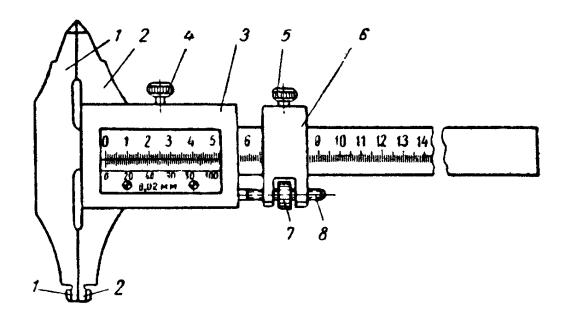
Внешний вид штангенциркуля ШЦ-II: 1 и 2 – губки с кромочными (сверху), плоскими и круглыми (внизу) измерительными поверхностями; 3 – рамка со шкалой нониуса; 4 и 5 – стопорный винт; 6 – устройство тонкой установки рамки (хомутик); 7 – гайка; 8 – винт
